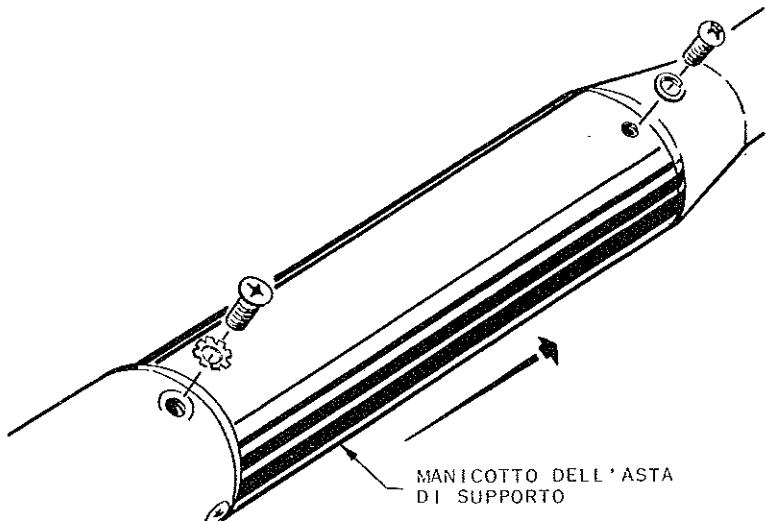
INSTALLAZIONE TUBO PITOT
